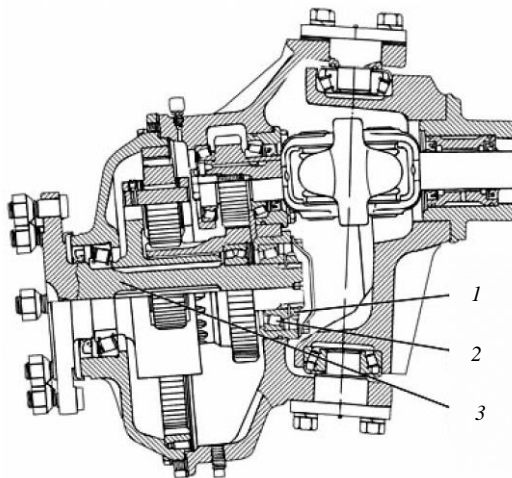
Проверка зазоров в подшипниках передних колес:
